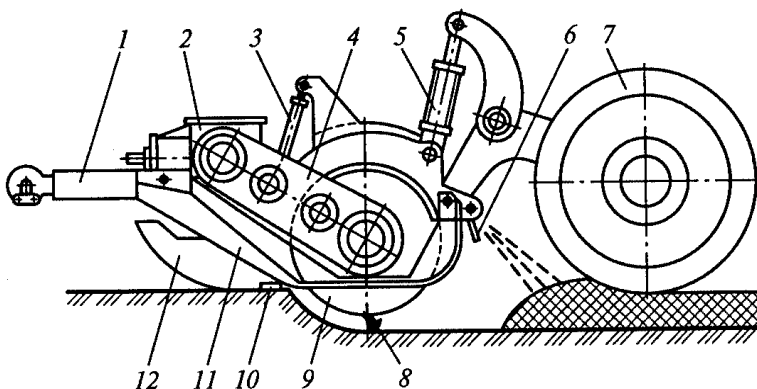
Машина лісова фрезерна МЛФ-0,8 [9]:
